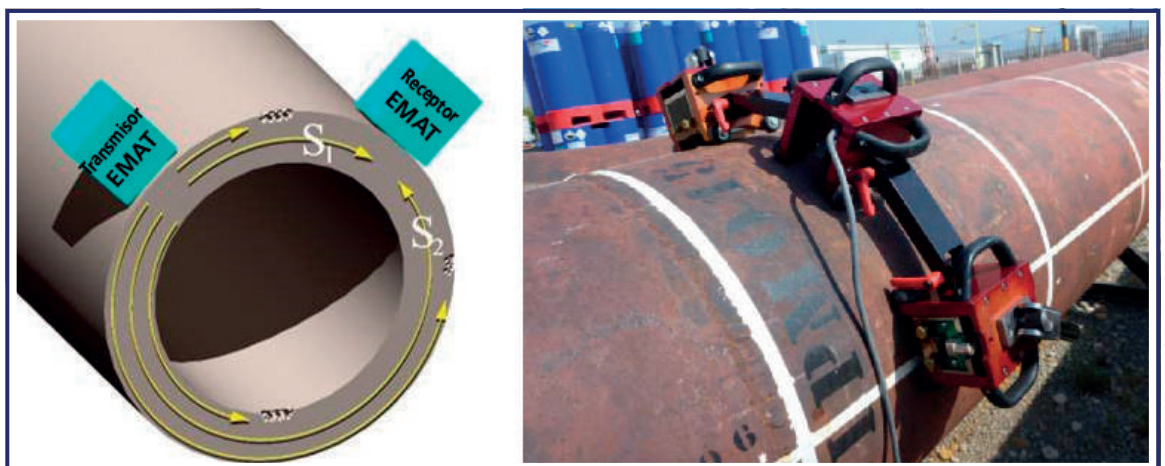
Esquema de configuración axial e inspección de tubería con ondas guiadas MRUT
